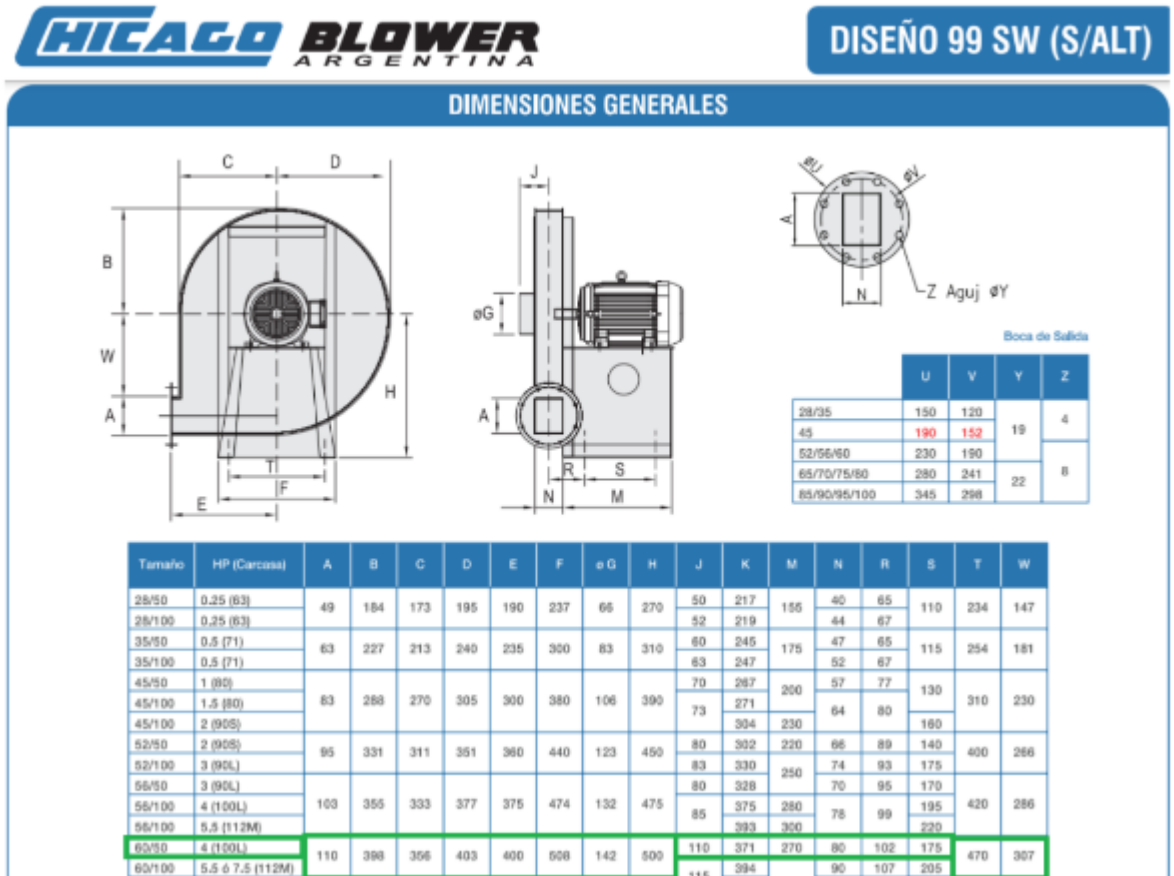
Especificaciones técnicas de soplador seleccionado. Fuente: Chicago Blower
